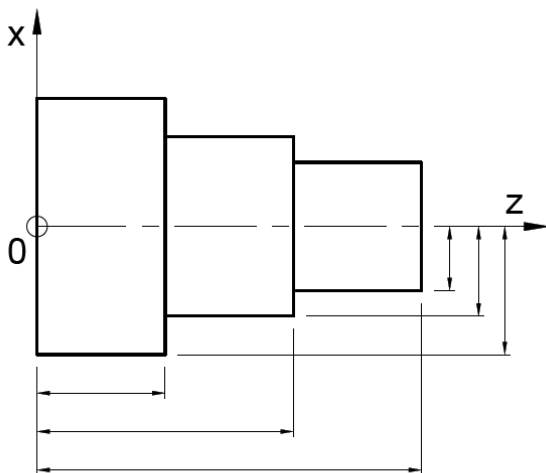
Schéma souřadnicové soustavy stroje LICO LND-65AY.
